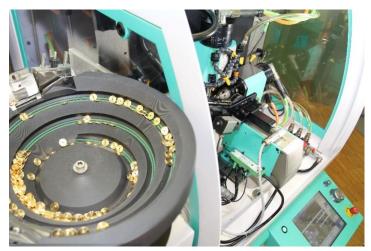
Caricatore a tamburo per pezzi di piccole dimensioni
